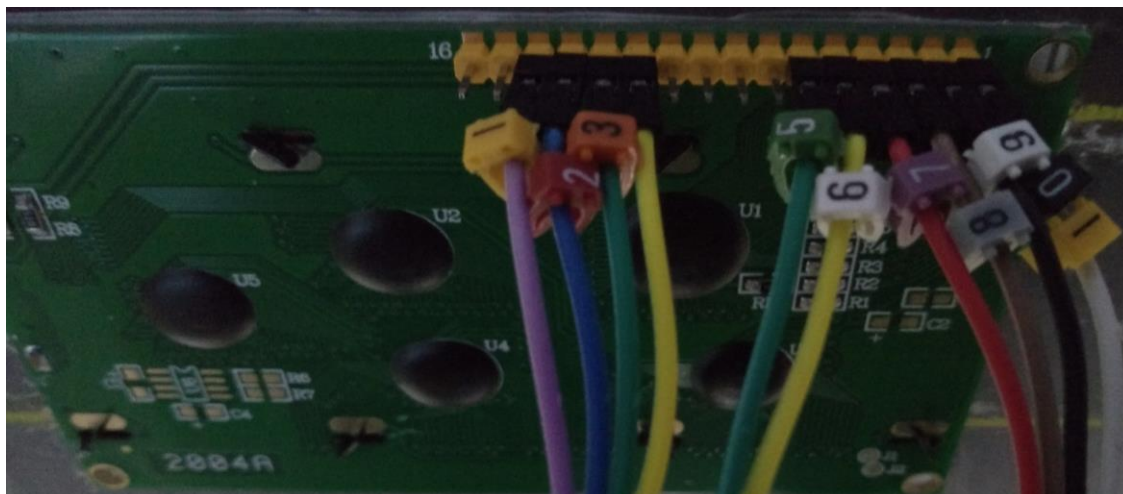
Marcado cables de control y alimentación. Fuente: [El Autor]
